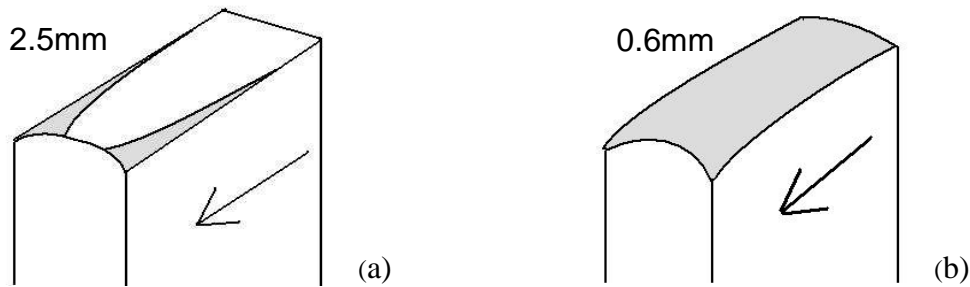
Schéma représentant la forme des surfaces de rupture pour les éprouvettes d'épaisseur 2.5mm (a) et 0.6mm (b)
